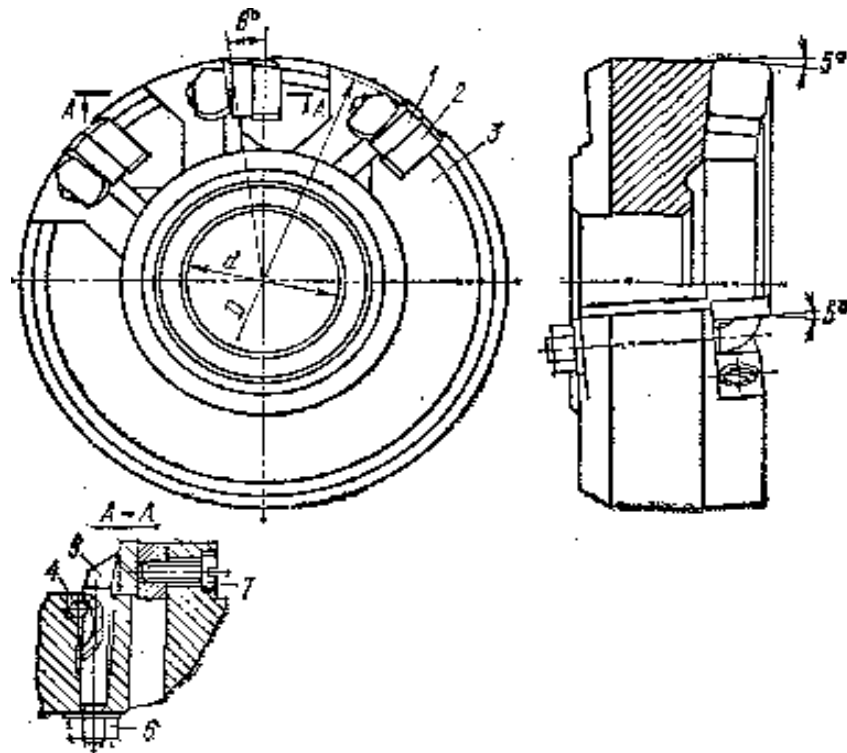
Торцева фреза з механічним кріпленням чотиригранних пластин із мінералокераміки
